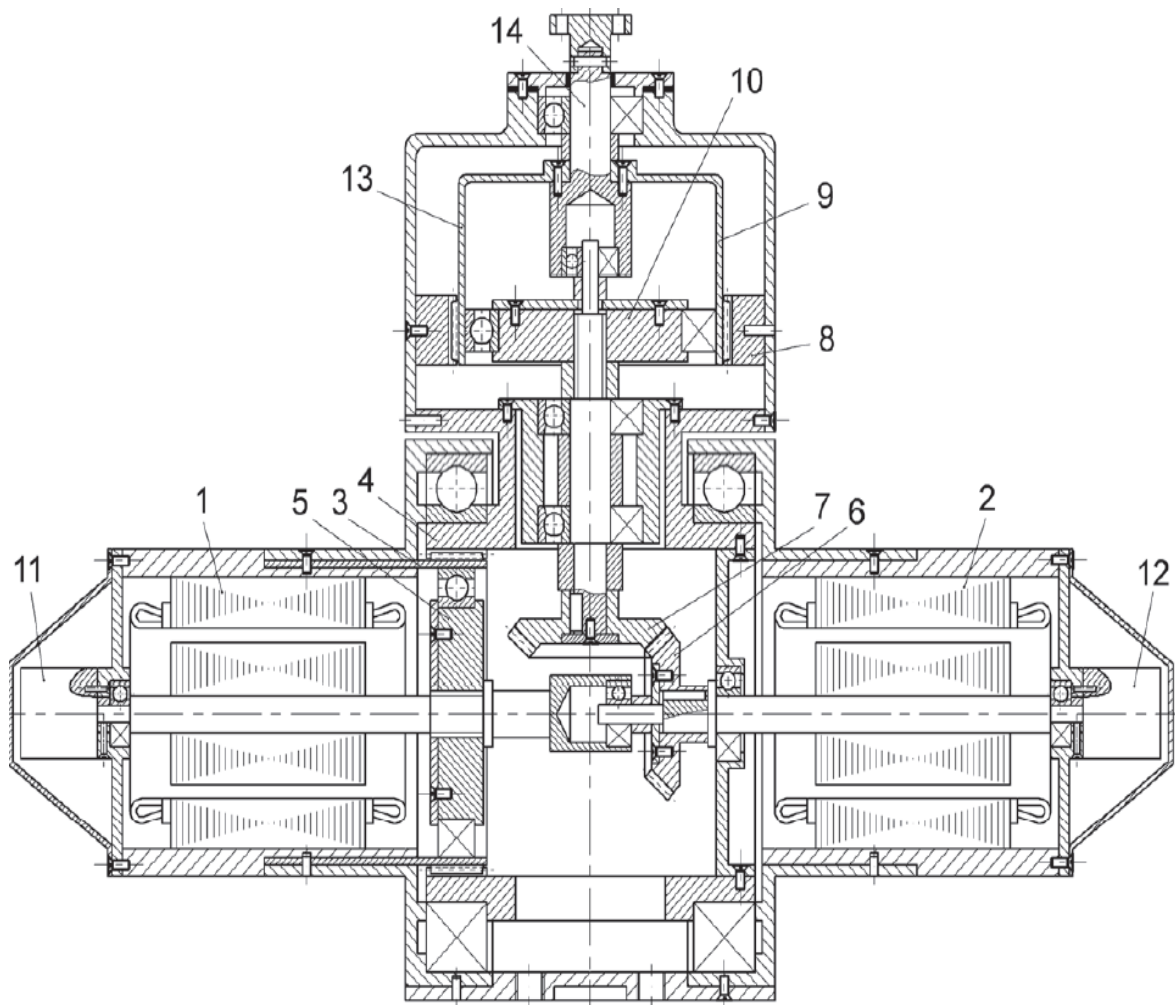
Двухкоординатный мехатронный модуль движения
